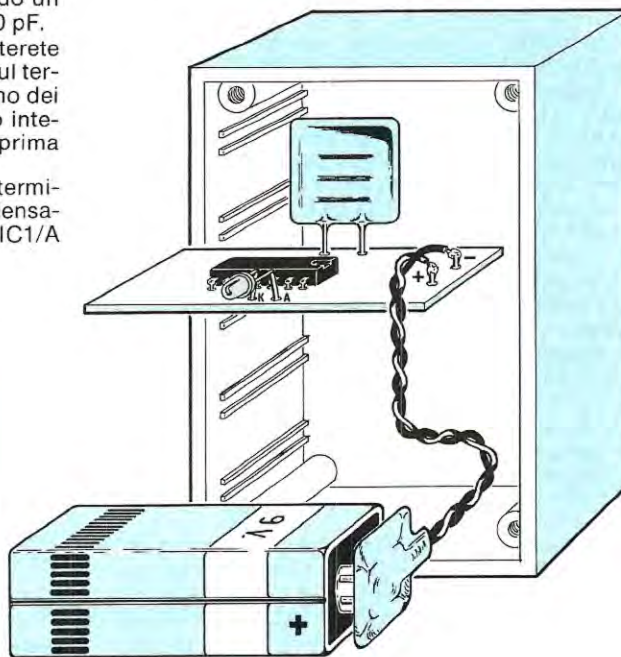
Il circuito stampato come vedesi in questo disegno e nella foto di sinistra deve essere infilato verticalmente nelle due guide presenti all'interno del mobile. Di lato il piano di foratura del pannello di alluminio.
